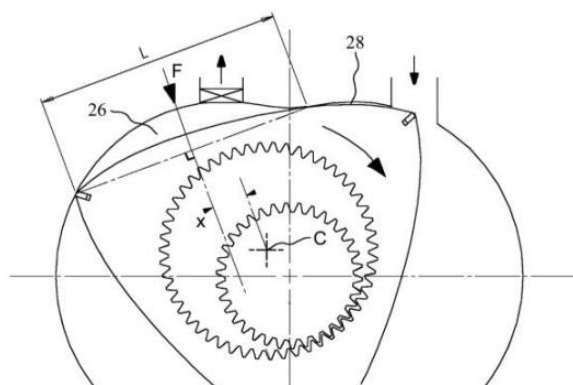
Прерывистая нагрузка крутящего момента на шестернях возникает из-за неравномерного давления газа на боковой поверхности ротора.
